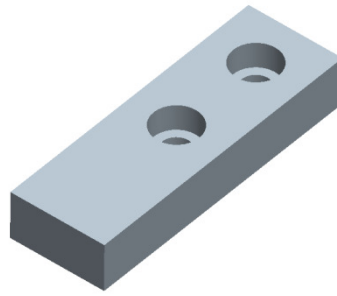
3D-Darstellung der Lagerplatte des Schwenkantriebes, erstellt mit Pro Engineer Wildfire 4.0. Die Lagerplatte dient der Befestigung des Schwenkantriebes an die Aluminiumprofile.
